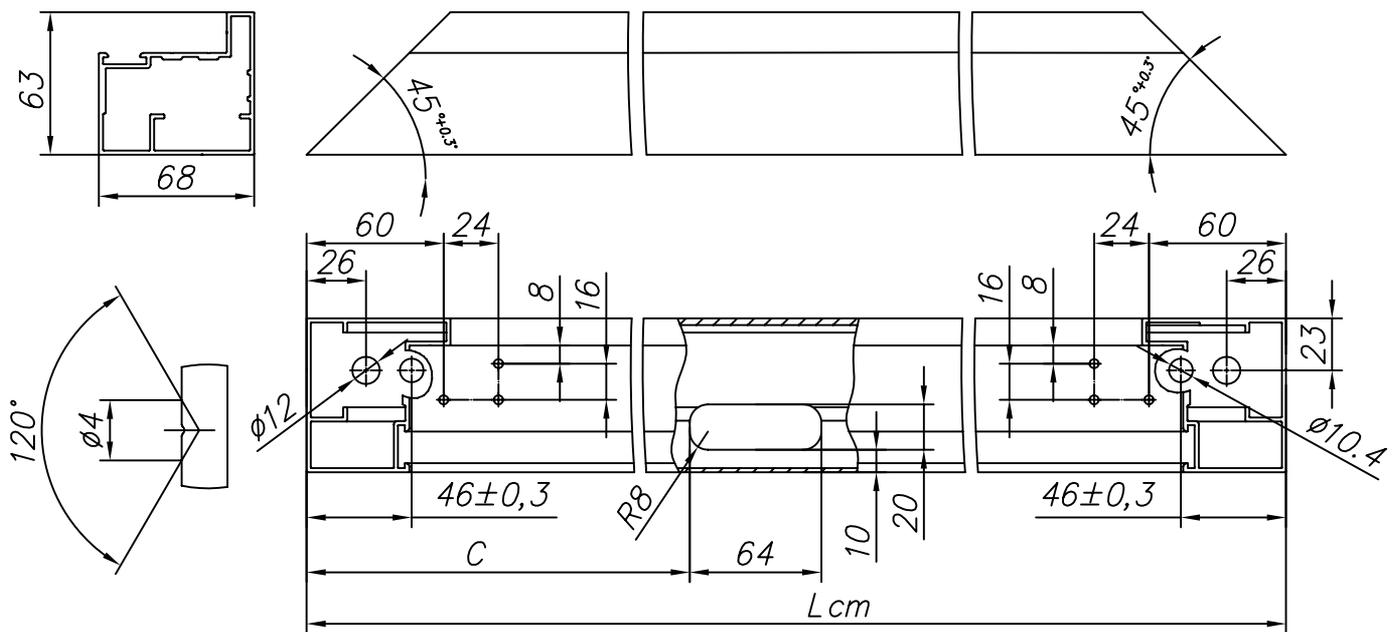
Изготовление стойки FLGU.400.0107 с пазом под ответную планку замка FLGU.400.1012 (открывание внутрь)
